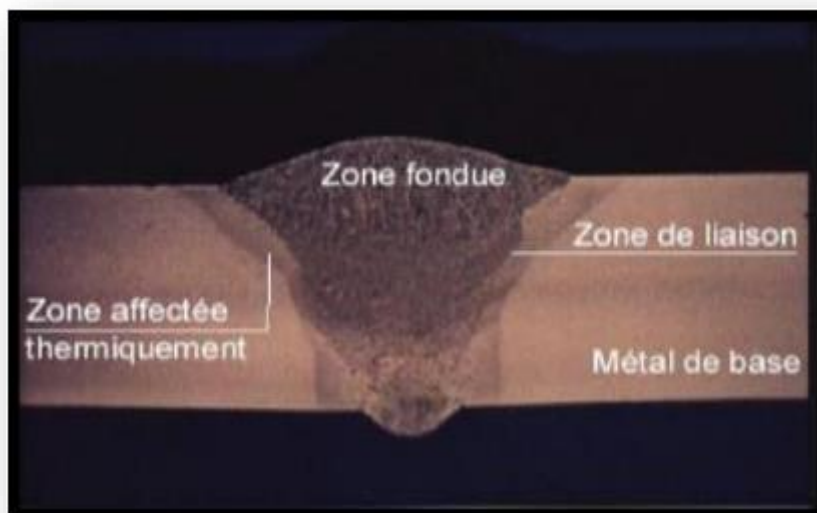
Présentation macrographique d'un joint soudé [49].
